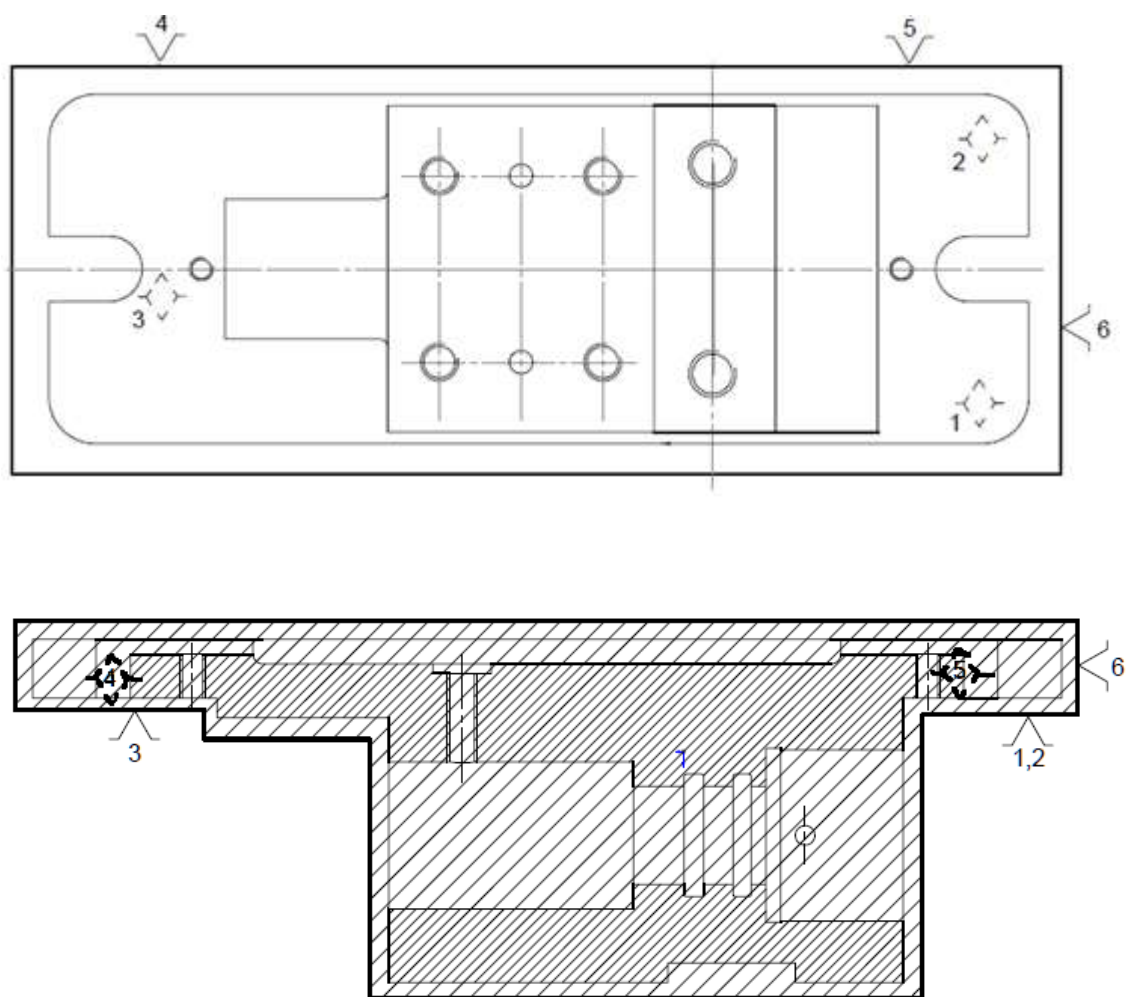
Теоретична схема базування по технологічним базам деталі «Корпус»
